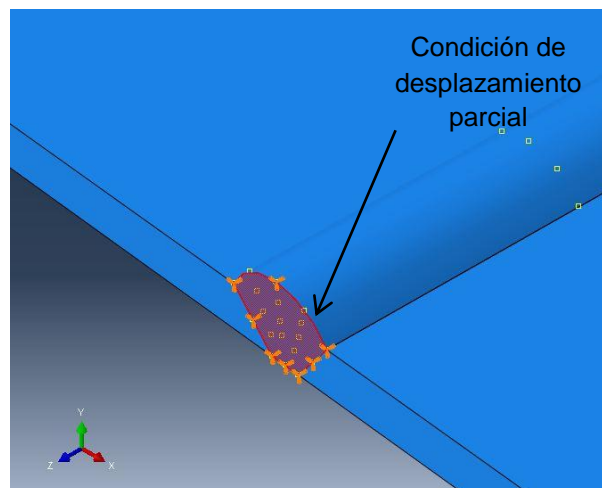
Área del modelo donde se ha aplicado la condición de frontera para simular el punto de soldadura que se le colocó a la junta antes de iniciar el proceso de soldadura.
